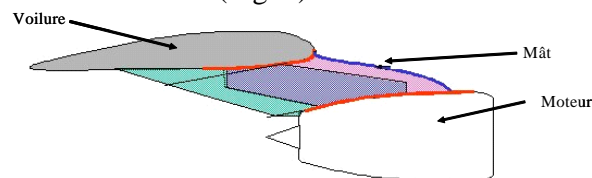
Vue d'ensemble du positionnement du mât moteur sur l'aile
